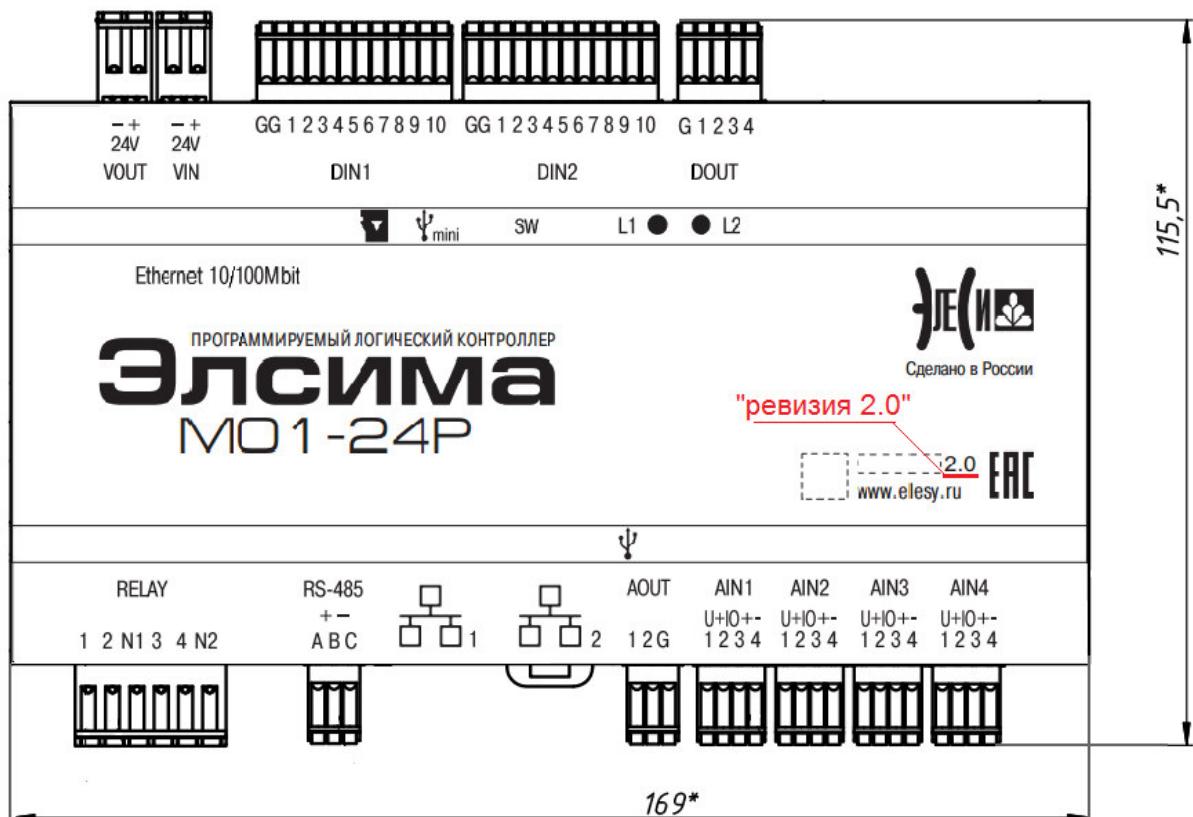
Контроллер Элсима. Габаритно-установочный чертеж. Вид спереди
